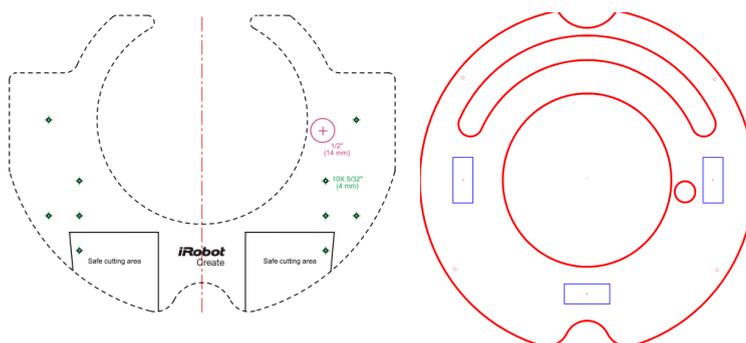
Tampa do manual do fabricante Roomba ao lado da projetada no Inkscape
